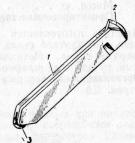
1 — корпус; 2 — нож; 3 — ролик
